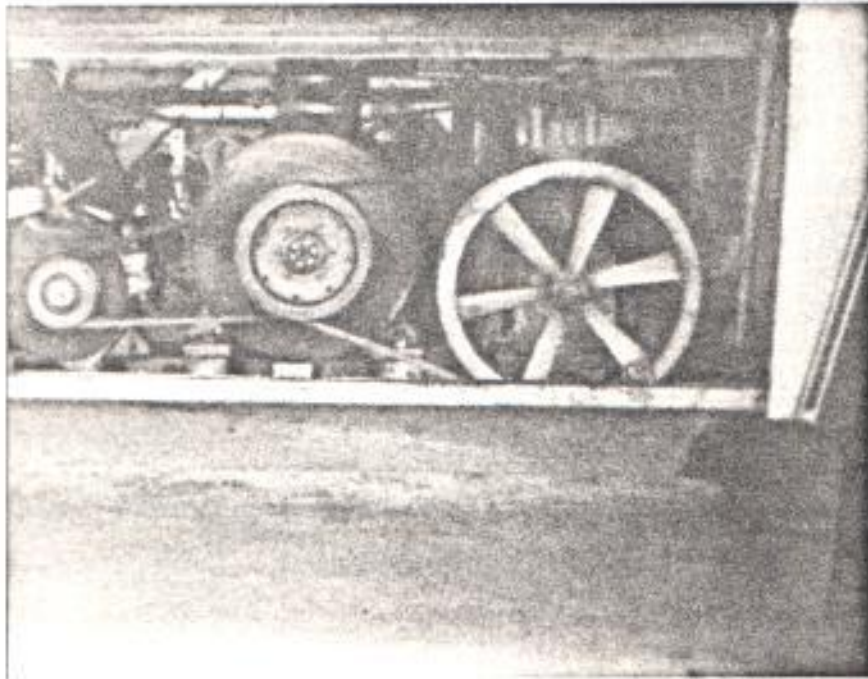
DISPOSICION DE LOS MOTORES AUXILIARES
